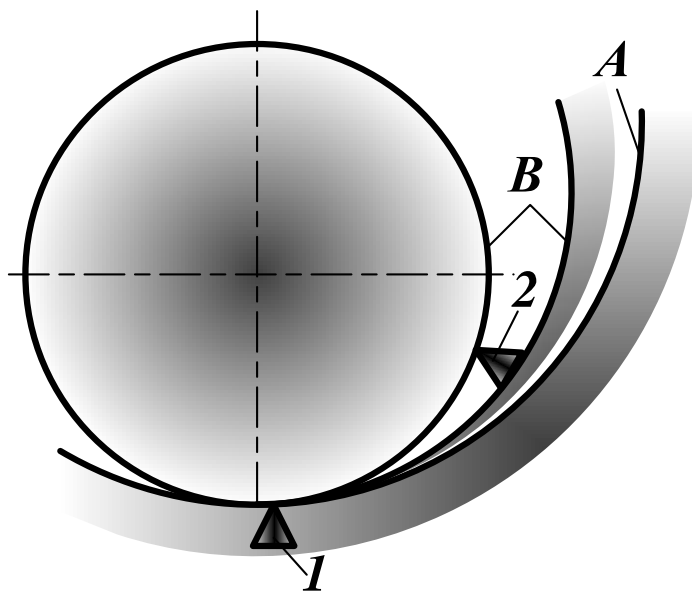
Схема абразивного изнашивания соединения вал-подшипник:
